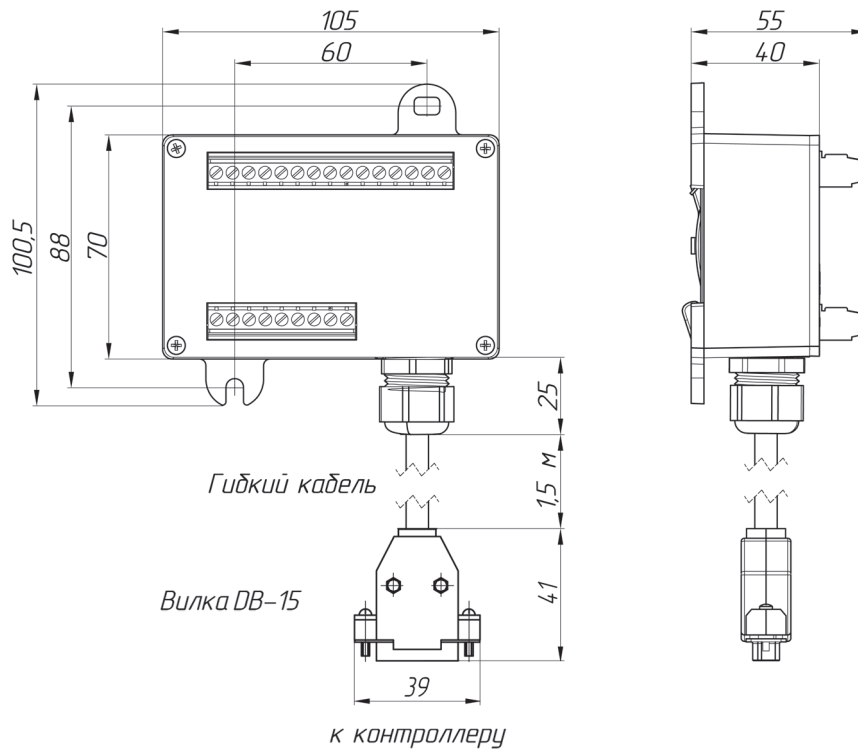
Внешний вид коробки клеммной: код вида 25
